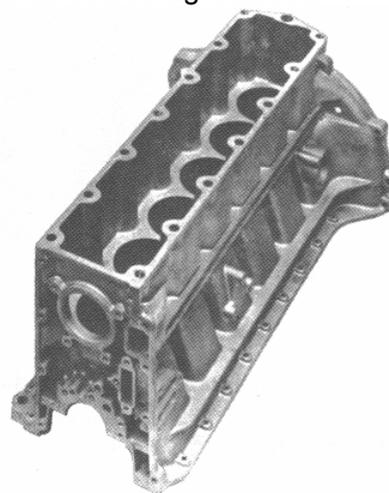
Bloque de motor de explosión de seis cilindros, colado en aleación ligera por fundición a presión.
